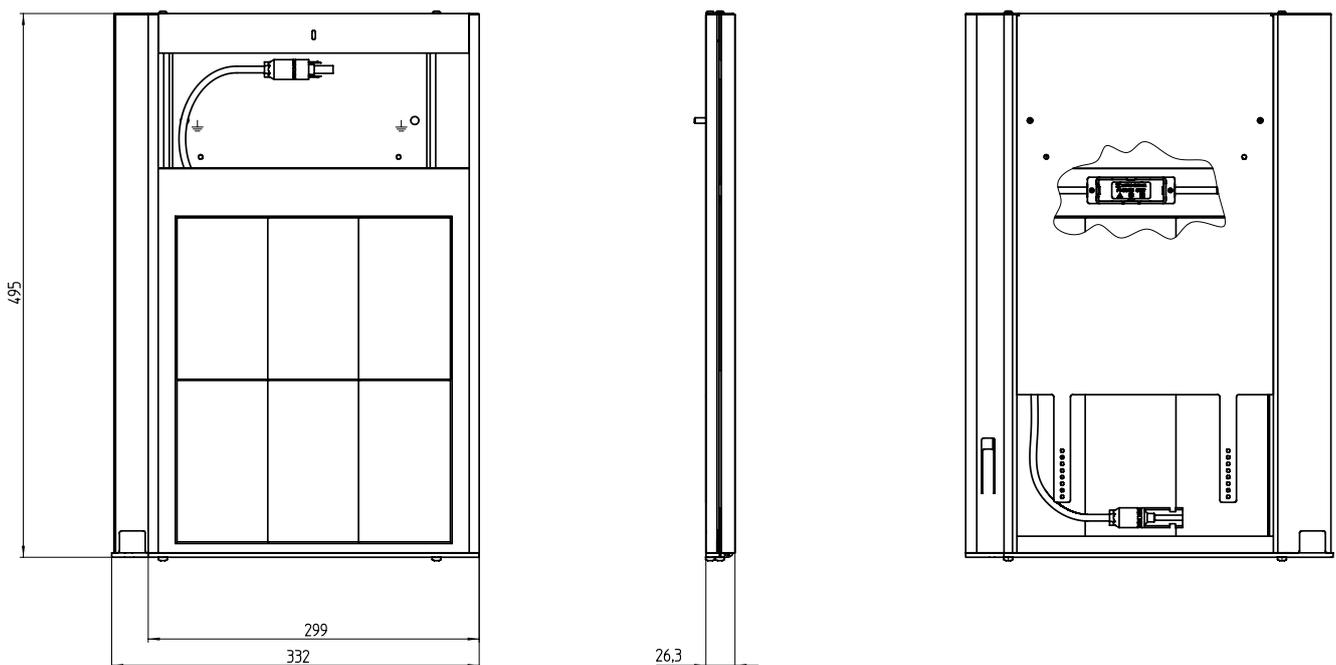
Technische Zeichnung des Meyer Burger Tile
